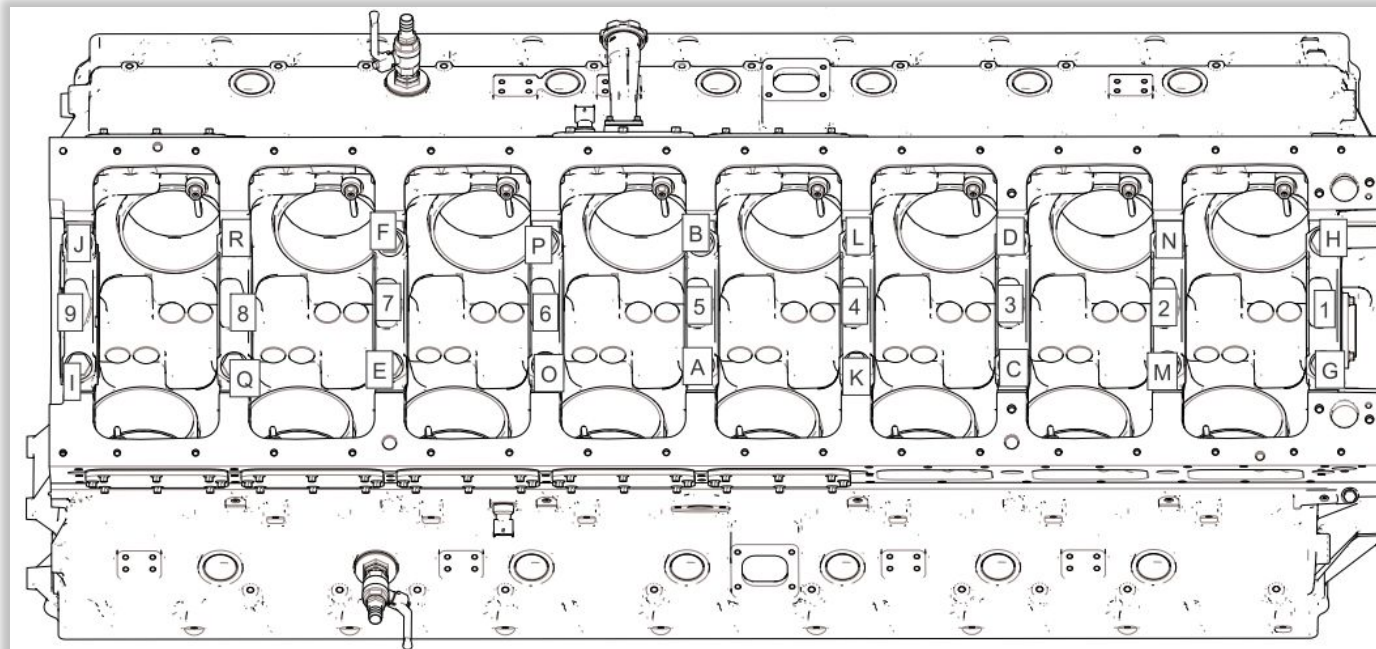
Последовательность затяжки болтов коренного подшипника 16М33.
